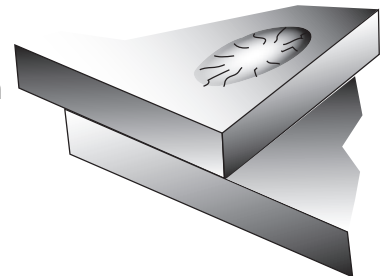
Joint typique pour le soudage à l'arc
